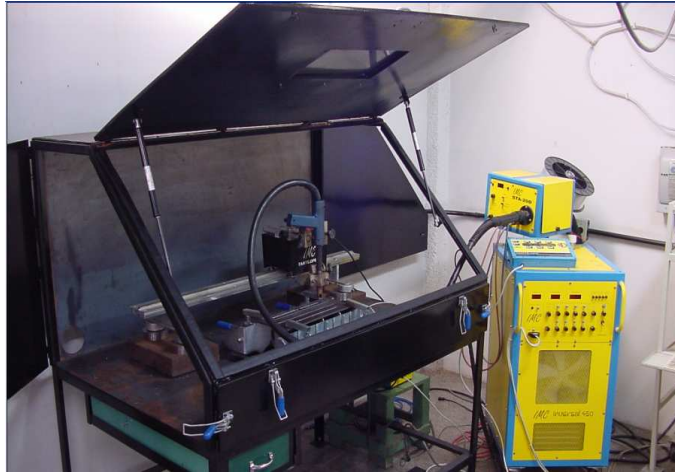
Bancada de ensaios de soldagem MIG CA do Labsolda – UFSC
